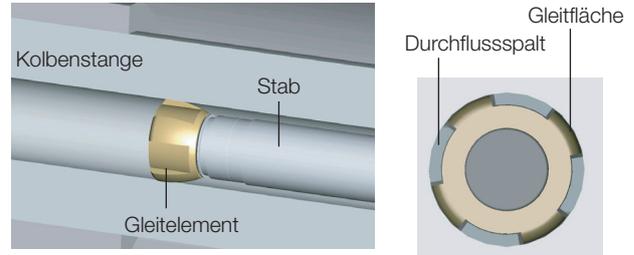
Detailansicht und Draufsicht Gleitelement
